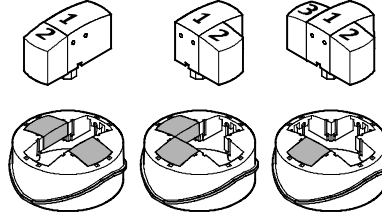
Uppbyggnad av lägesindikeringen – exempel
